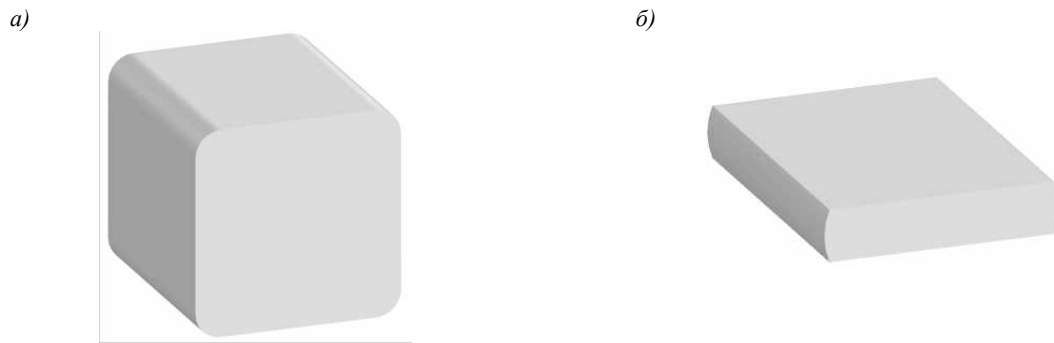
Сталева заготовка 80 x 80 мм (а) та готовий виріб - смуга 15×65 мм (б)
